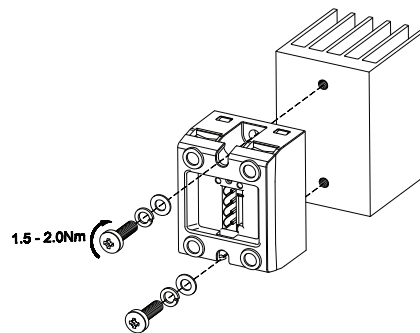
Befestigungsschrauben M5 abwechselnd bis max. 0.5 Nm anziehen und anschließend bis max. 2.0 Nm fortsetzen. (Der Einsatz von Unterlegscheiben mit Sprengring ist zu empfehlen), siehe Zubehör (Schraubenkits).
